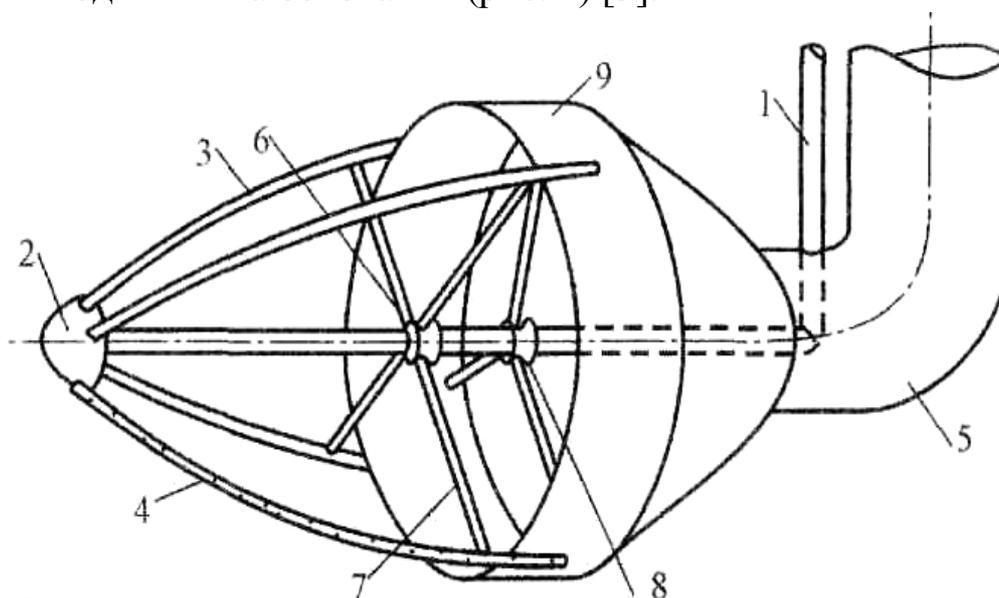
Гидродинамический оголовок НГМА: 1 – напорный водовод к струеобразователям; 2 – раздаточная камера; 3 – струеобразователи; 4 – отверстия; 5 – всасывающий водовод; 6 – подшипник; 7 – ребра жесткости; 8 – крепление к корпусу; 9 – корпус в виде раструбного переходника
